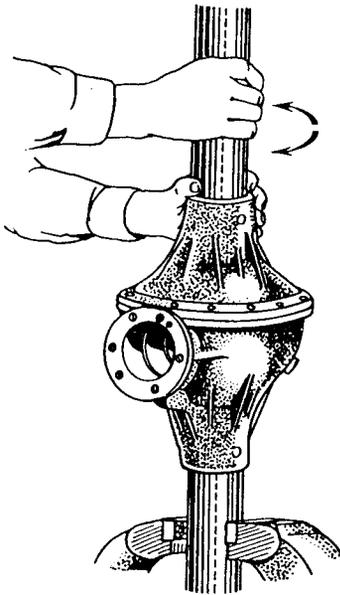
Einlaufen der Lagerrollen im Ausgleichgetriebe
